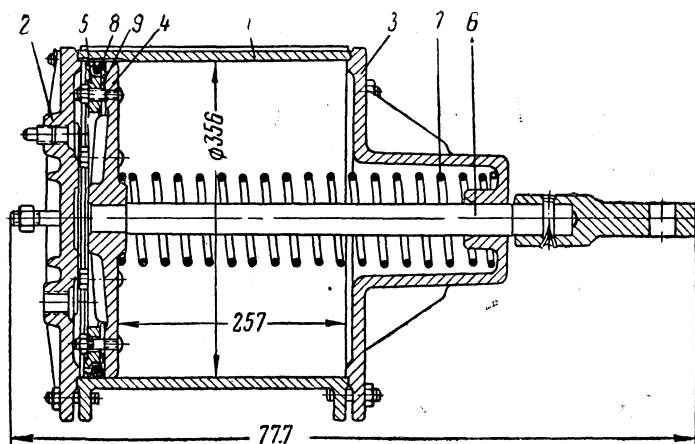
Тормозной цилиндр усл. № 435 без кронштейна для тройного клапана
